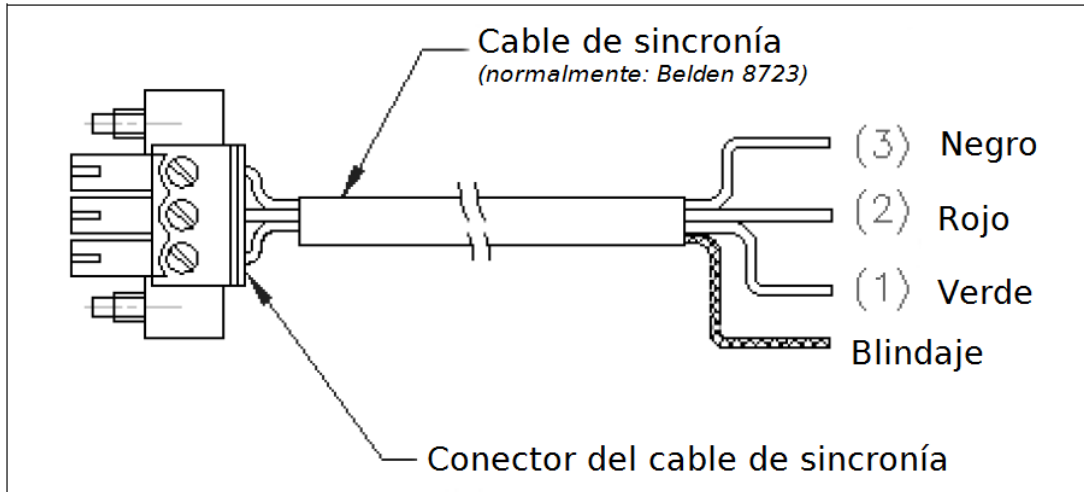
Ensamble de un mini-conector al cable de sincronización.
